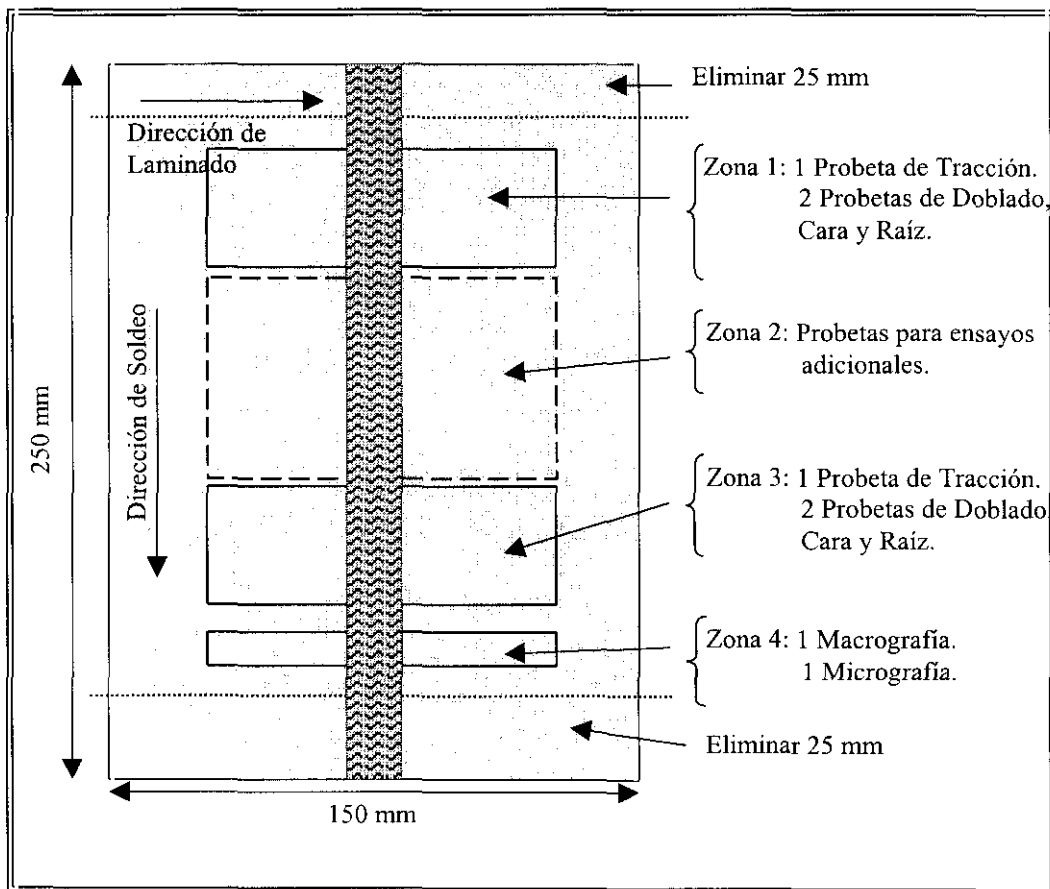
Localización de las probetas de ensayo en un cupón de soldadura a tope.
